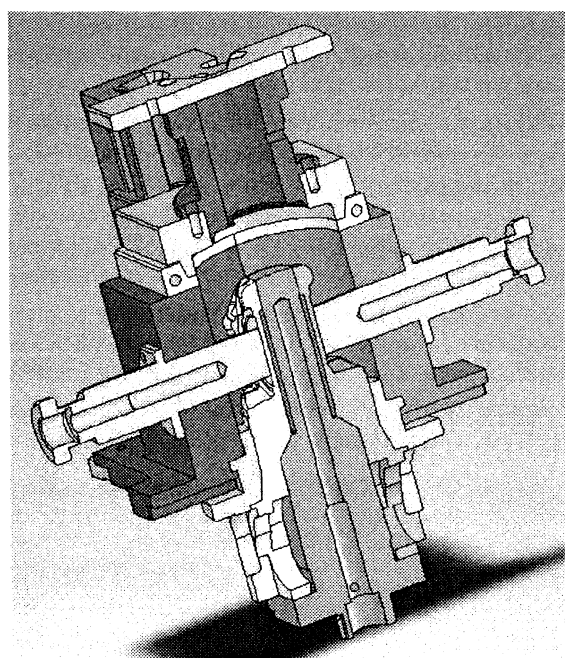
Конструкция типовой кокильной оснастки для производства поршней
